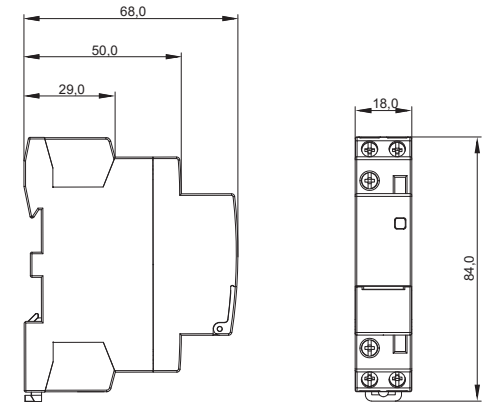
Габаритные размеры контакторов до 25 А, 2P / Figure 1 – Overall dimensions of contactors up to 25 A, 2P
